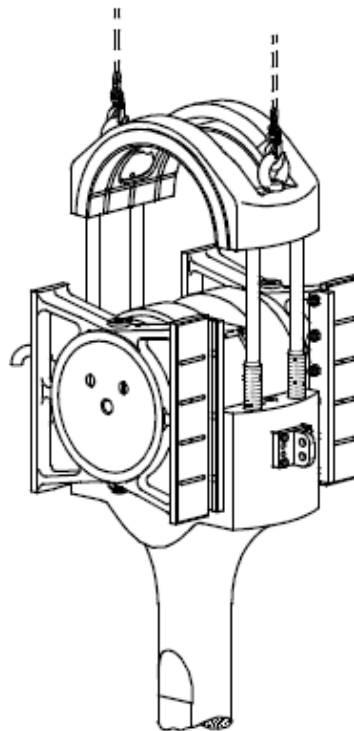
Від'єднання кришки крейцкопфного підшипника
